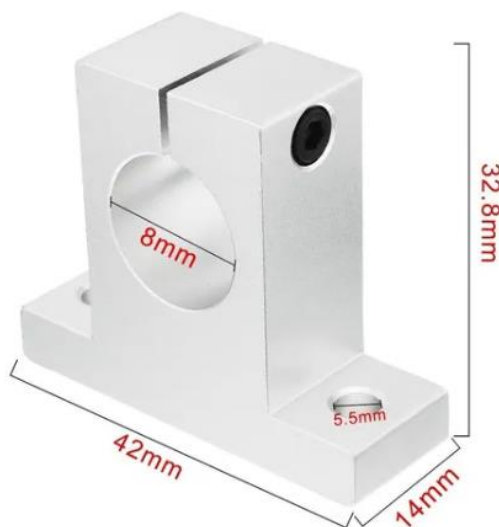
Dimensiones del soporte – Mecatronix
